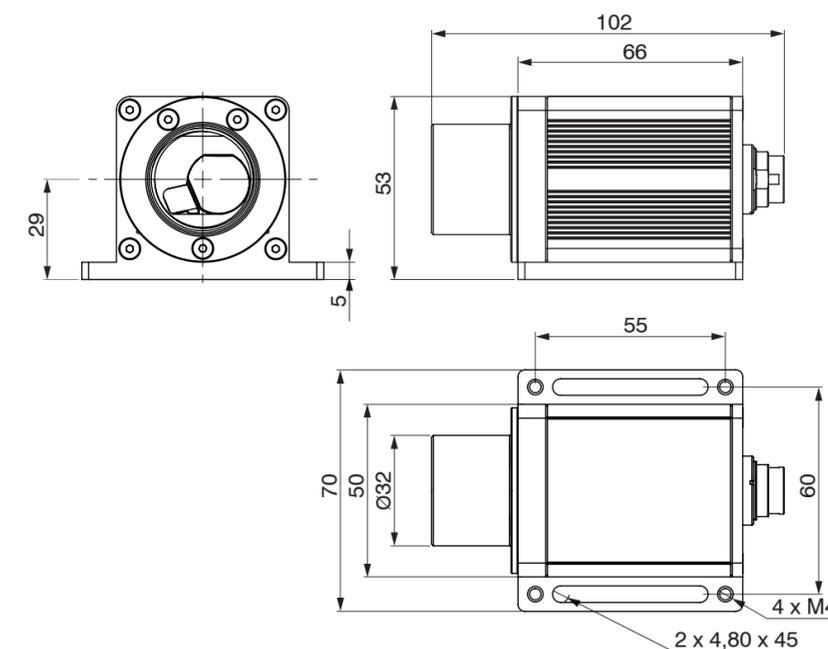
Maßzeichnung optoNCDT ILR2250-100, Abmessungen in mm
